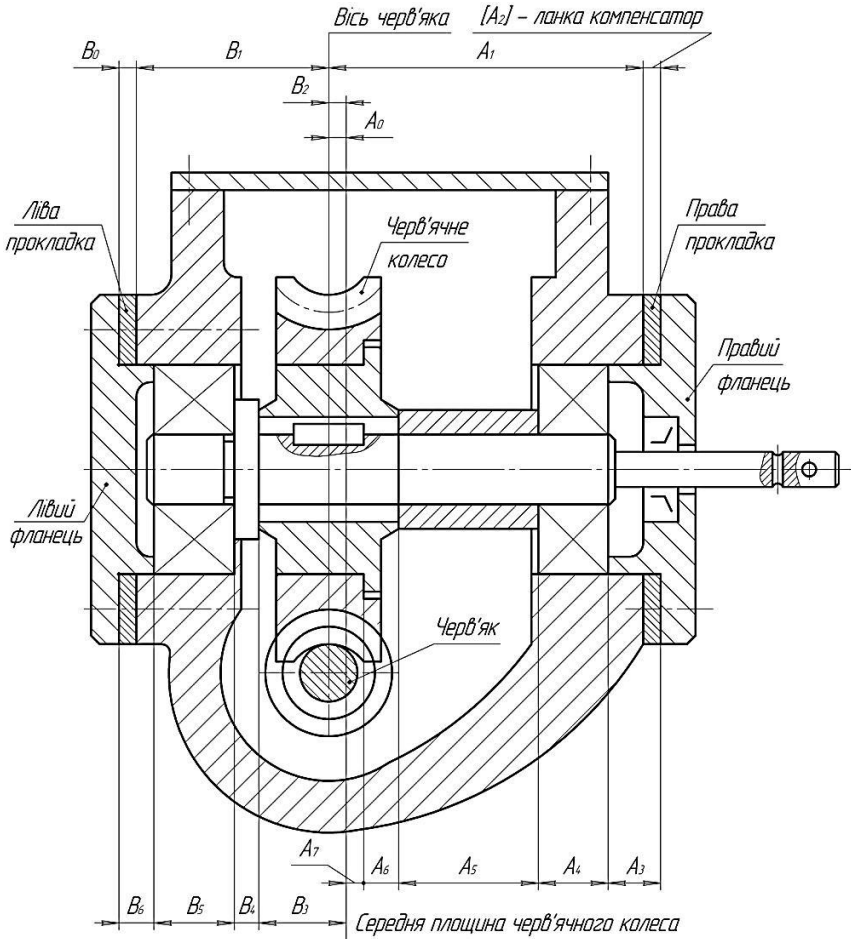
Розмірні ланцюги, які визначають збіг середньої площини черв'ячного колеса із віссю черв'яка
